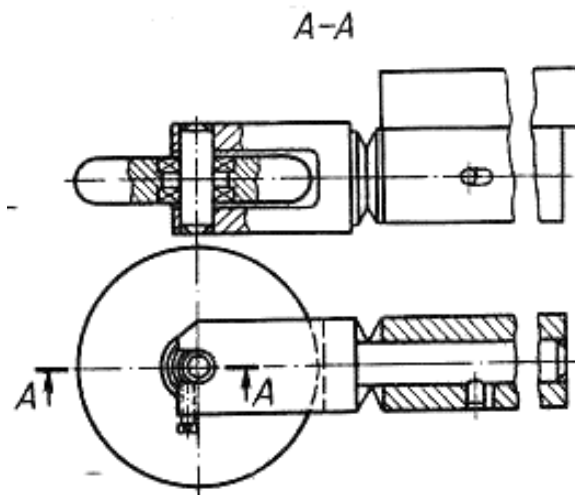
Пристрій з тарілчастими пружинами для формоутворення зовнішніх канавок [21]
